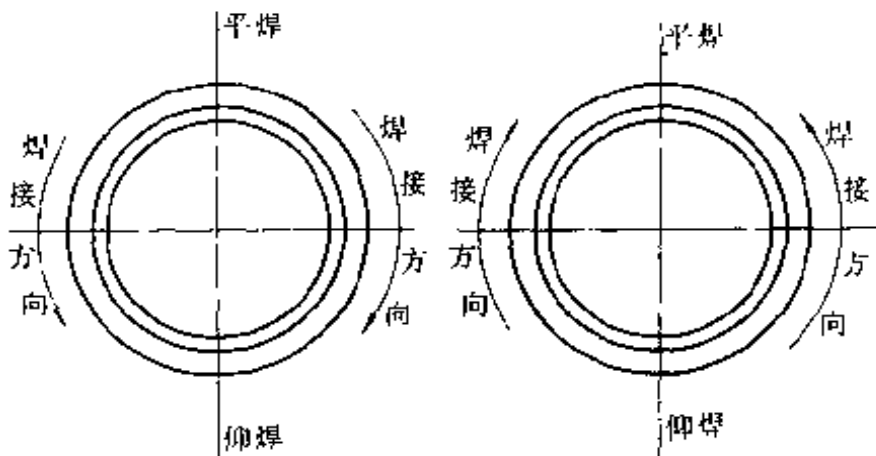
小管水平固定外填丝 TIG 焊焊接路线
